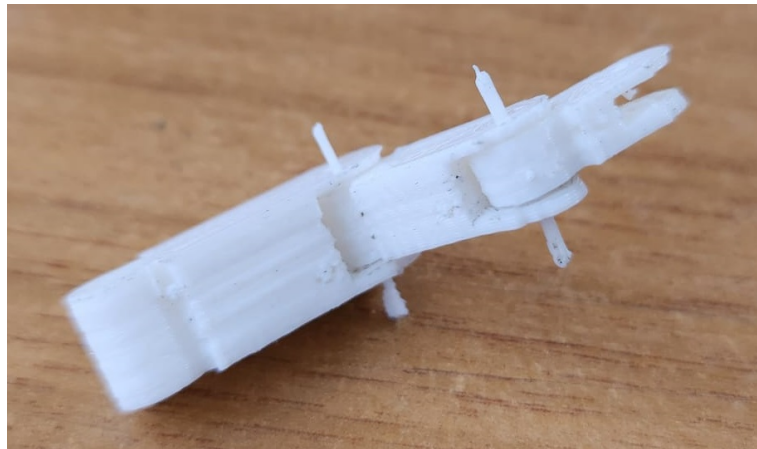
Ensamblaje de pines con tolerancia de 0.6 y 0.7 mm.
